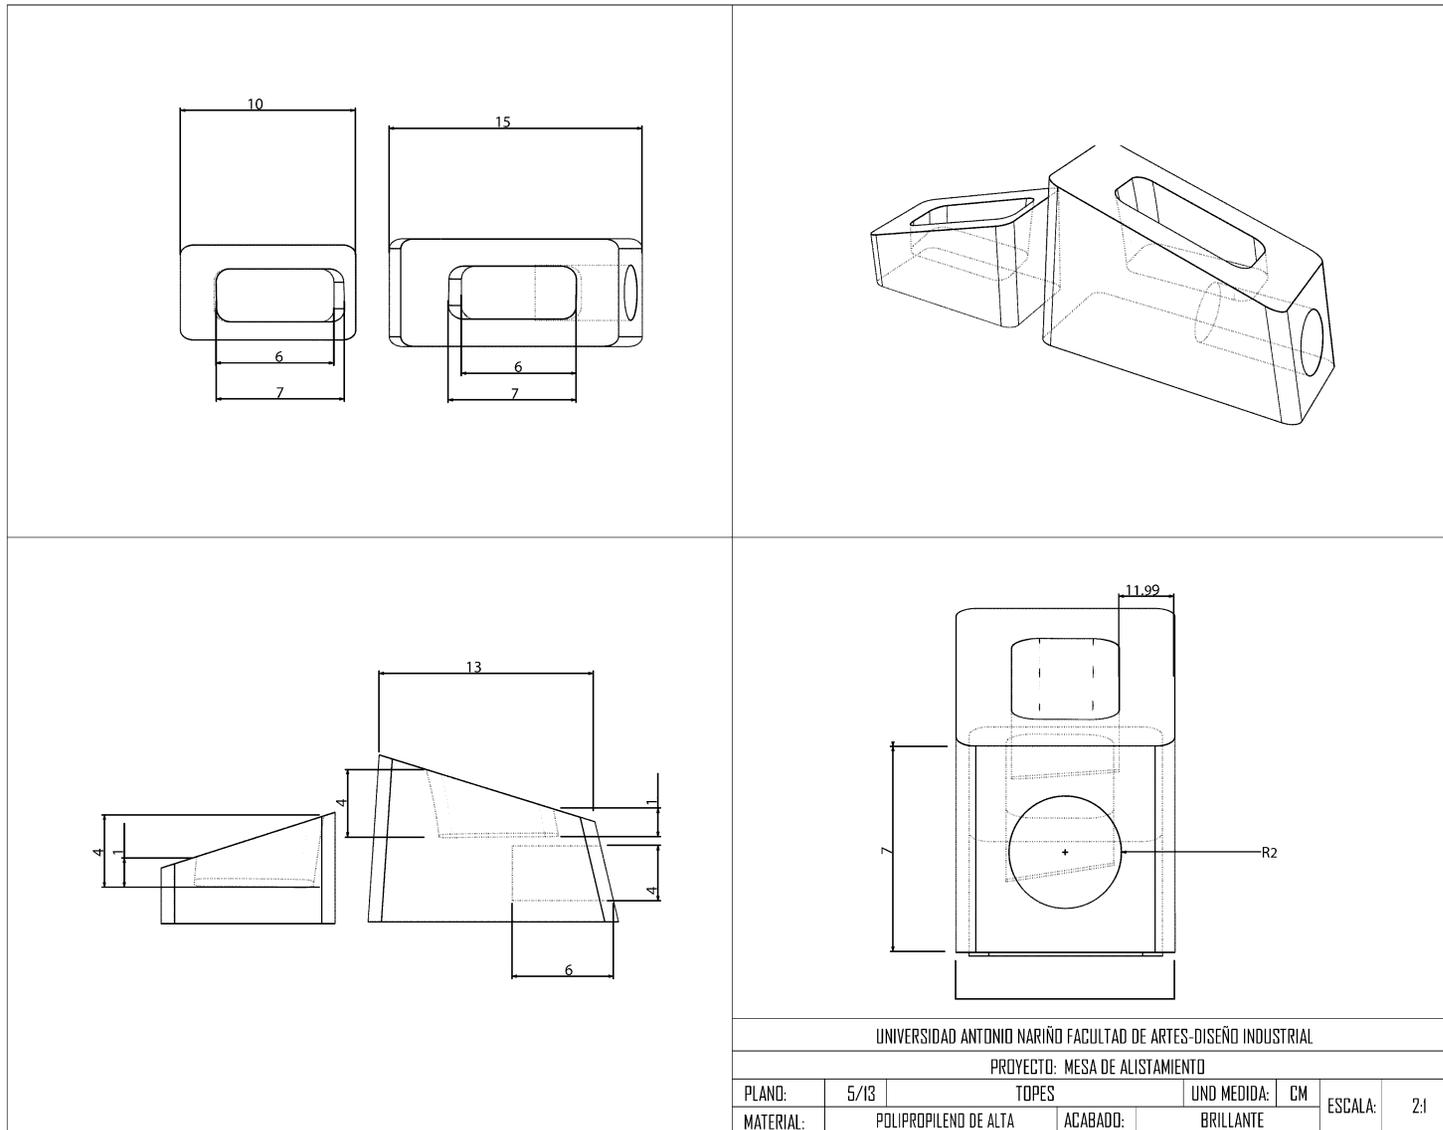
Planos piezas 4 (Elaboración propia, 2020)
